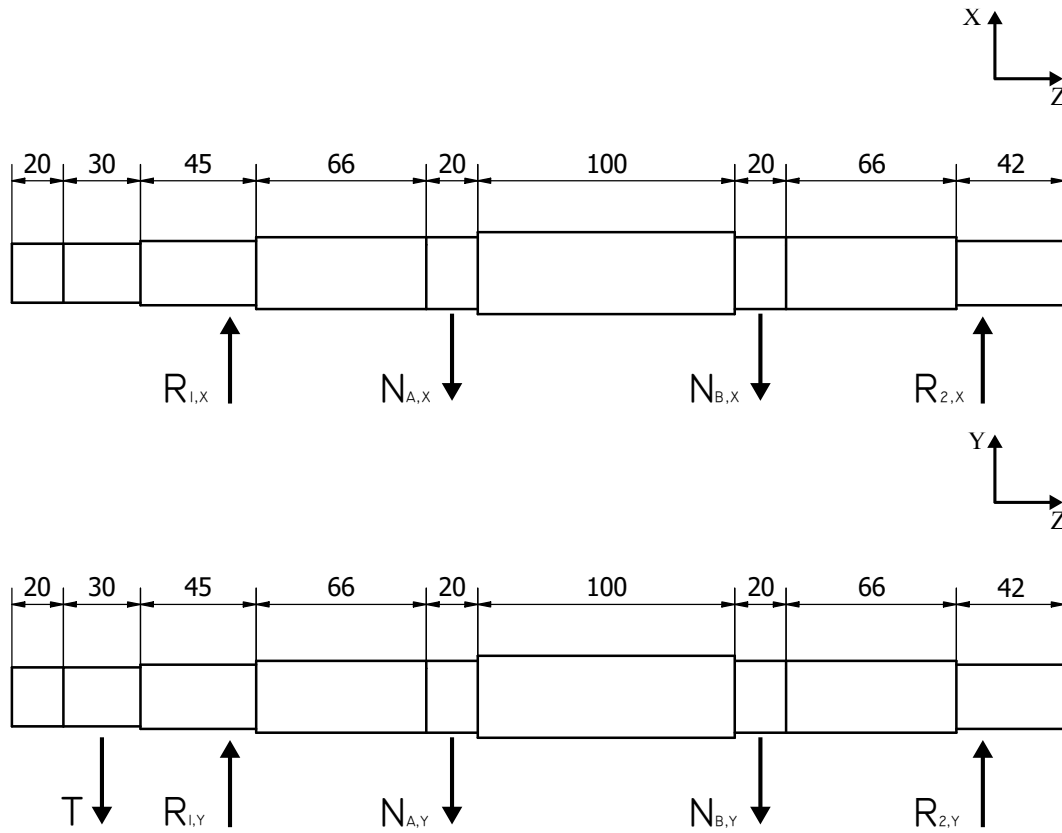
Fuerzas aplicadas en el eje derecho del banco de ensayos. Imagen superior, plano XY. Imagen inferior, plano XZ.
